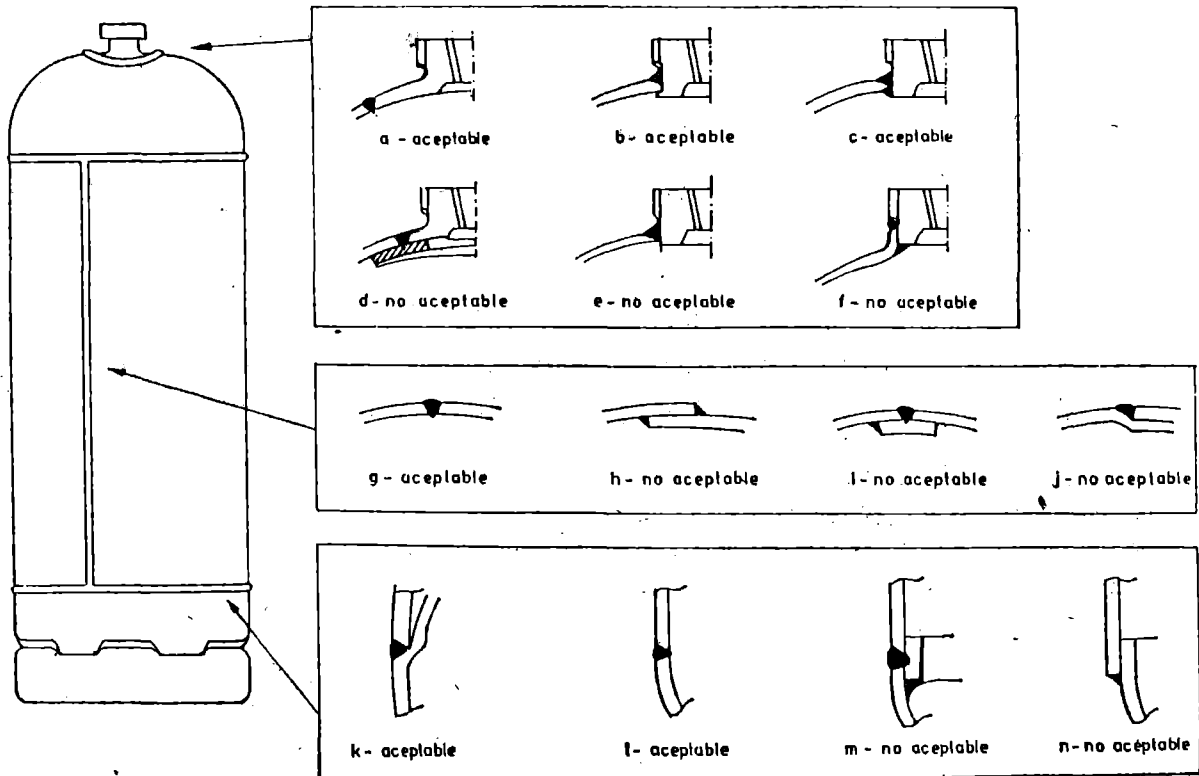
SOLDADURAS ACEPTABLES Y NO ACEPTABLES
